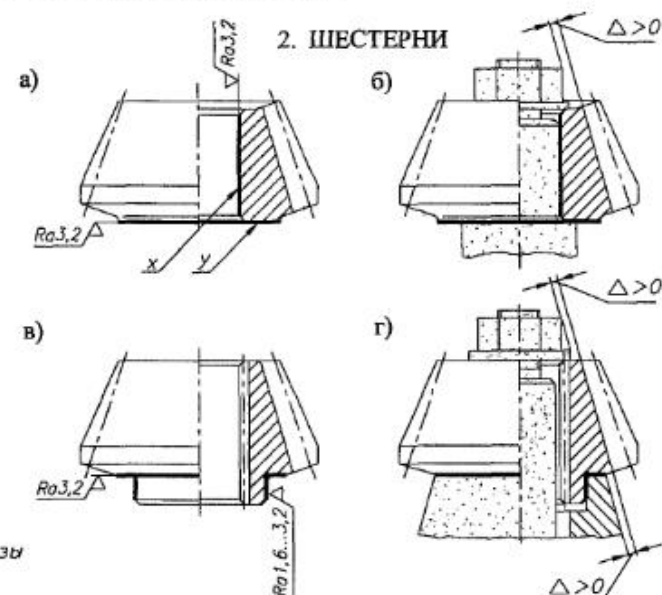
Установочные базы для нарезания зубьев на шестернях
